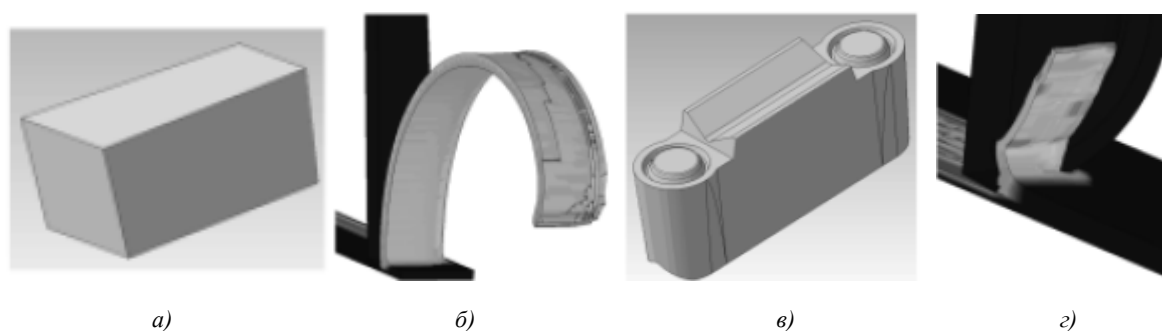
Форма режущего инструмента и форма стружки при обработке
